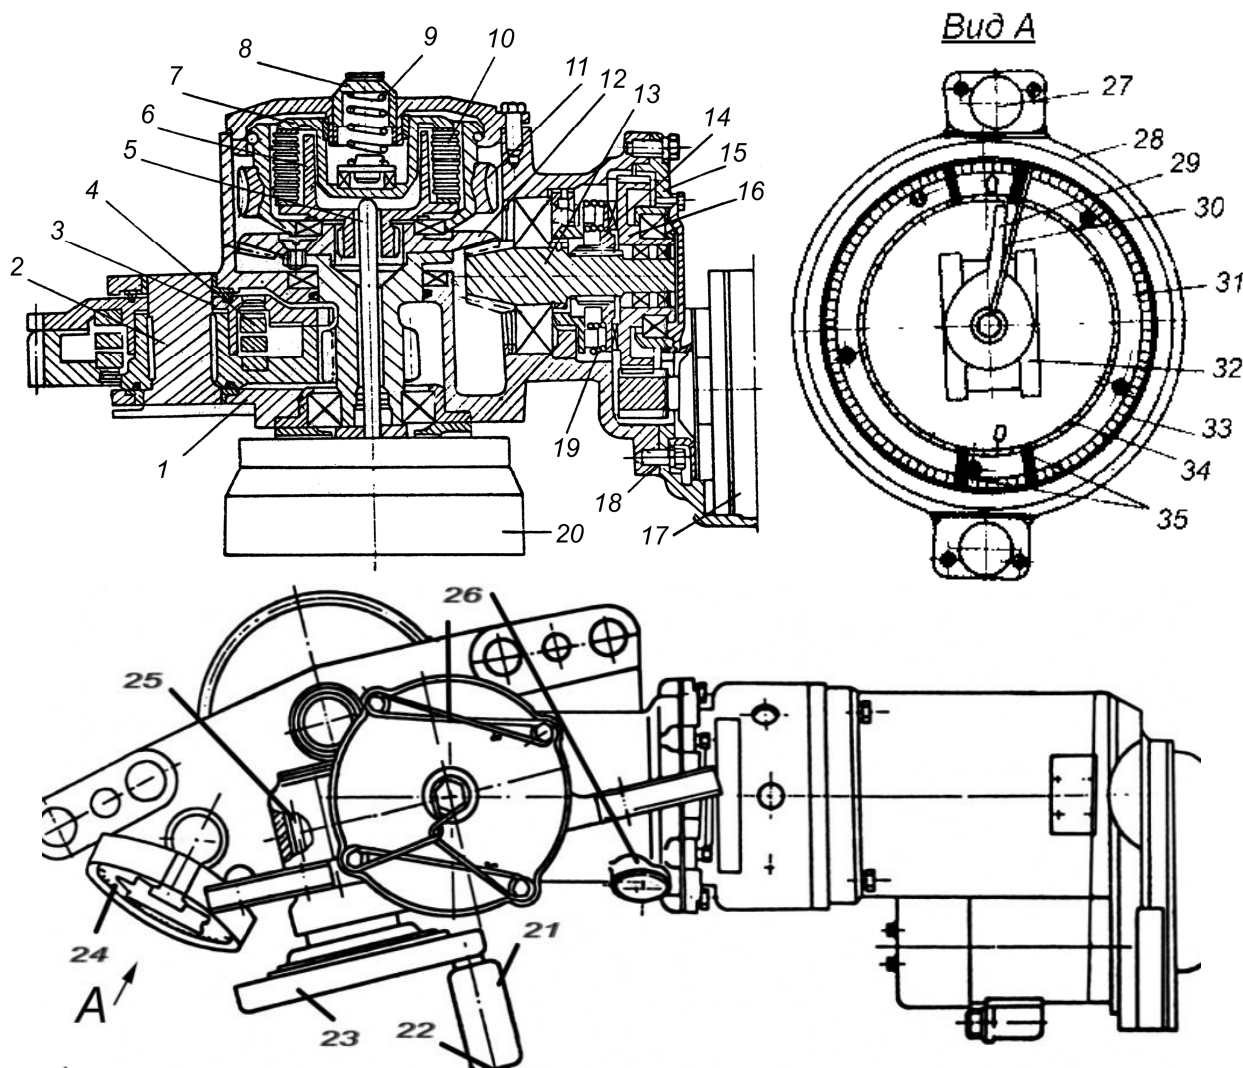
Электромеханический механизм поворота и азимутальный указатель: 1 – картер; 2 – эксцентриковая ось; 3 – разрезная шестерня; 4 – пружина; 5 – шток; 6 – ведомый барабан со шлицами; 7 – нажимной барабан; 8 – пробка; 9 – пружина; 10 – диски фрикциона; 11 – червячная шестерня; 12 – коническое колесо; 13 – коническая шестерня; 14 – подвижная полумуфта сдвигующего звена; 15 – горловина; 16 – шестерня с
